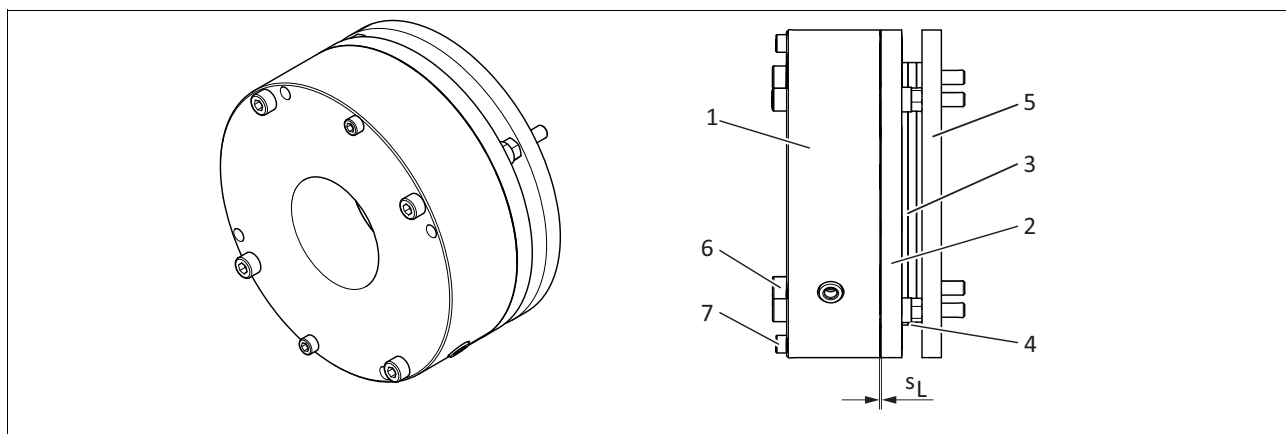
Aufbau einer Federkraftbremse INTORQ BFK457-16 Compact, komplett montiert Rotor und Flansch
